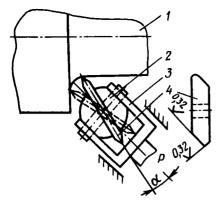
Приспособление для обкатки галтелей шатунной шейки коленчатого вала:
